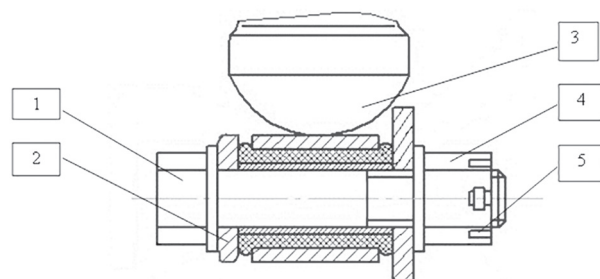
Схема крепления амортизатора в разрезе: 1 – болт, 2 – корпус сиденья, 3 – амортизатор, 4 – шайба, 5 – гайка
